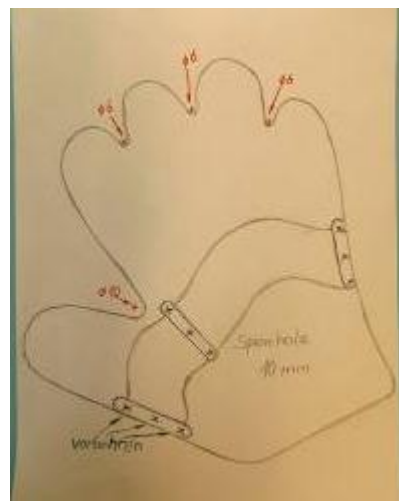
Technische Freihandzeichnung mit Bemaßung der Bohrungen
